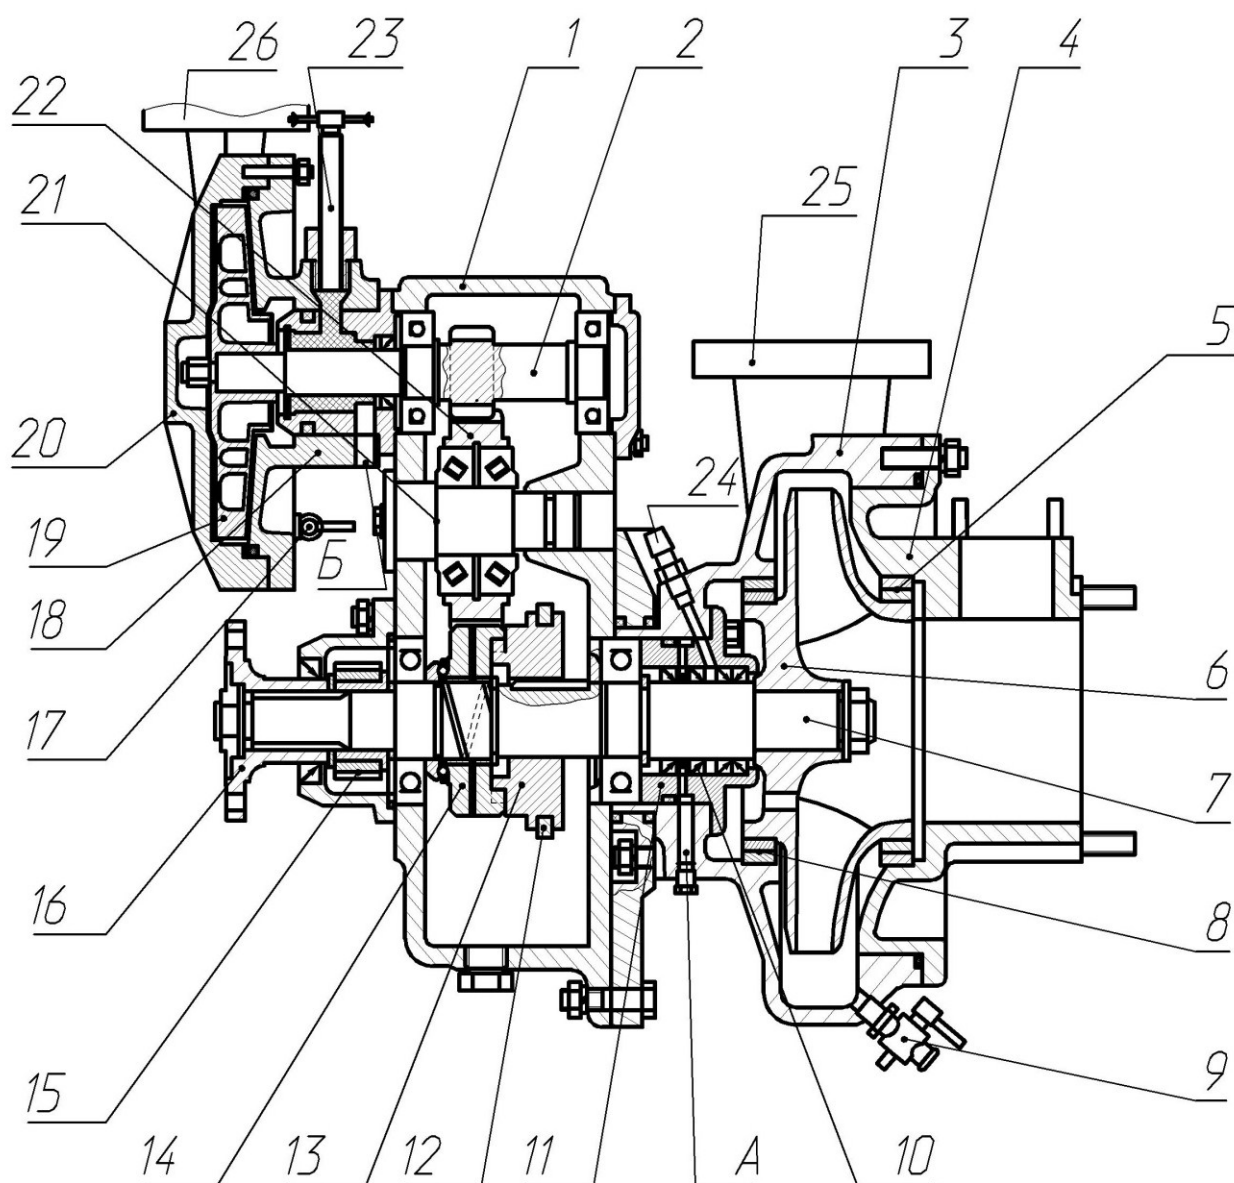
Пожарный комбинированный насос ПНК-40/3: 1- корпус повышающего редуктора; 2 – вал ступени высокого давления; 3 – корпус ступени нормального давления; 4 – крышка ступени нормального давления; 5 – уплотнение торцевое; 6 – рабочее колесо ступени нормального давления; 7 – вал ступени нормального давления; 8 – торцевое уплотнение; 9 - кран сливной из ступени нормального давления; 10 – манжеты резинокаркасные; 11 – уплотнительный стакан ступени нормального давления; 12 – вилка включения ступени высокого давления; 13 – муфта включения ступени высокого давления; 14 – шестерня ведущая ступени высокого давления; 15 – привод тахометра; 16 – фланец привода насоса; 17 – сливной краник ступени высокого давления; 18 – корпус ступени высокого давления; 19 – рабочее колесо ступени высокого давления; 20 крышка ступени высокого давления; 21 – ось; 22- шестерня
